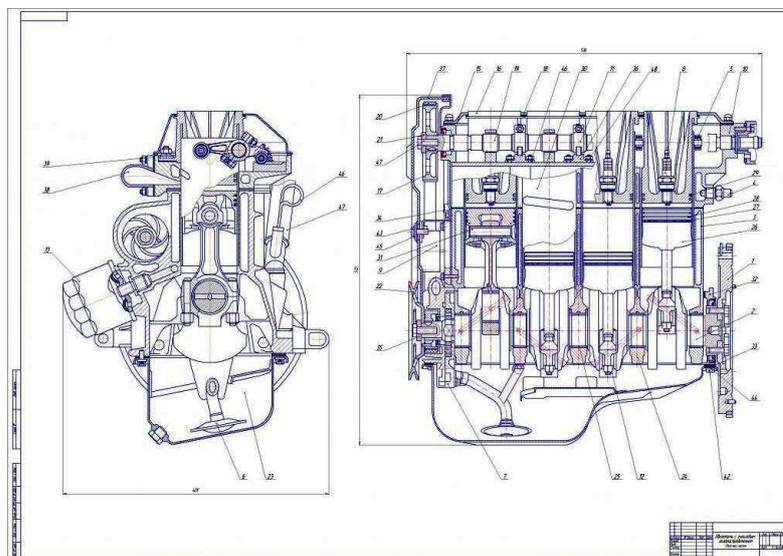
Сборочный чертеж двигателя внутреннего сгорания
